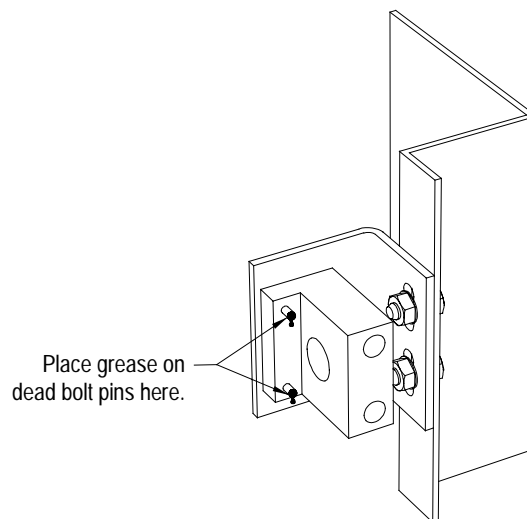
Schließbolzengegenstück, montiert am Schrank
